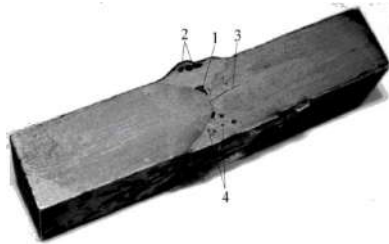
Макроструктура якісного зварного з'єднання багатошаровою ручною електродуговою зваркою при Y-подібній підготовці крайок з підваренням кореня шва
